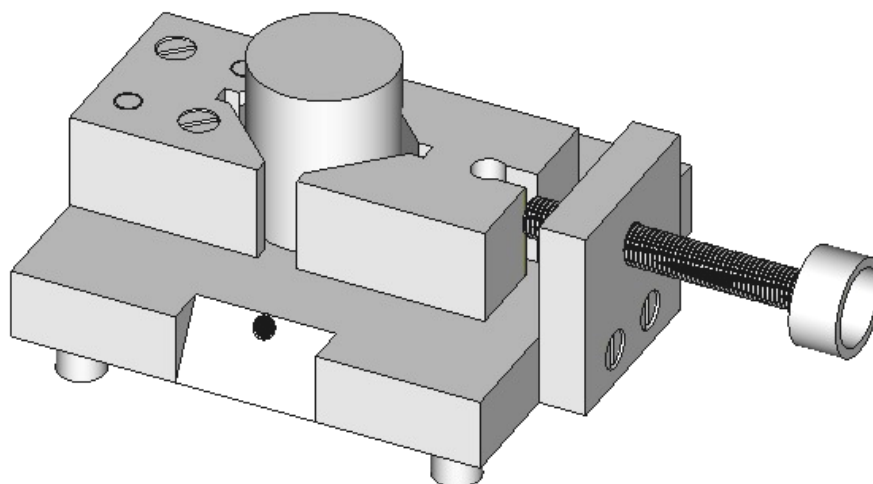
Установка заготовки с упором в неподвижную призму
